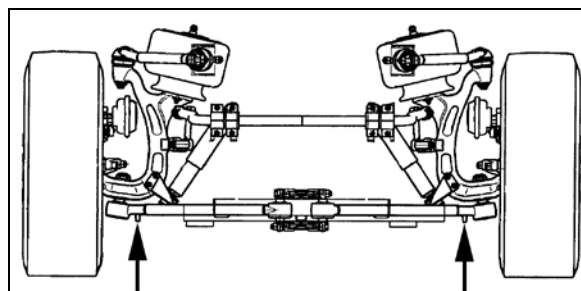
POINTS DE LEVAGE SUR LA SUSPENSION INDÉPENDANTE
